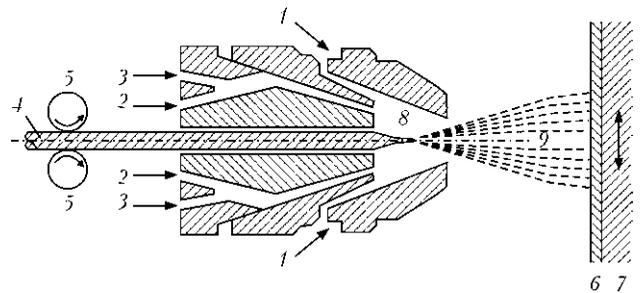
Схема газопламенной горелки согласно норме DIN EN 657 [3]: 1 — сжатый воздух; 2 — горючий газ; 3 — кислород; 4 — проволока или пруток; 5 — протяжный механизм; 6 — напыляемое покрытие; 7 — подложка; 8 — оплавляемый конец проволоки; 9 — поток расплавленных частиц
